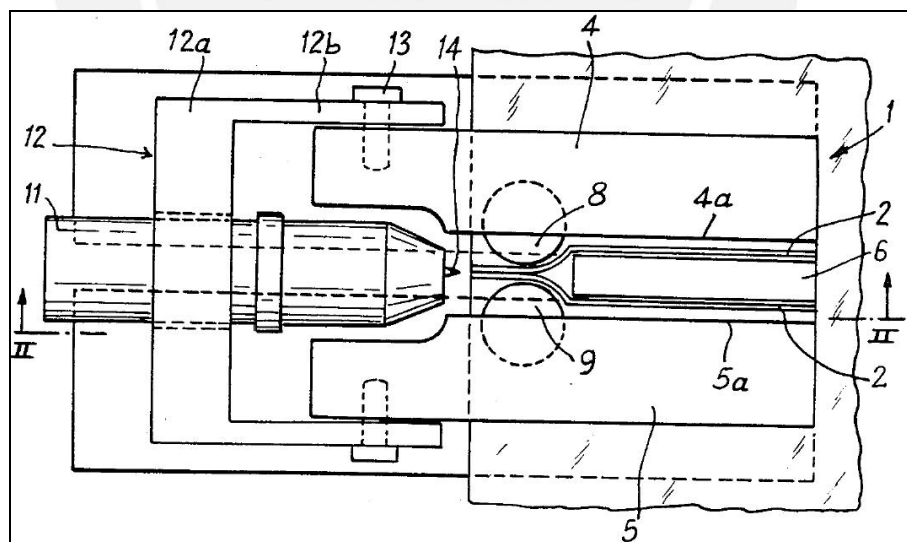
Esquema de una Maquina plegadora y soldadora de aristas [8]
